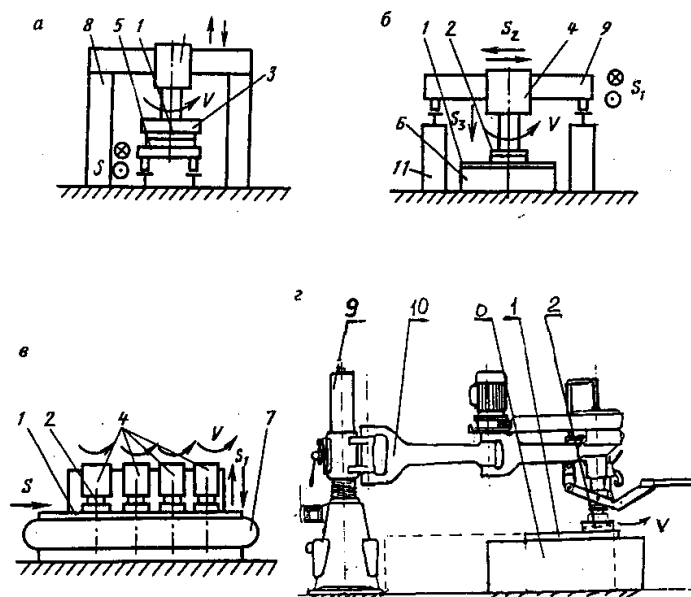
Схемы шлифовально-полировальных станков: а — порталного; б — мостового; в — конвейерного; г — коленно-рычажного (колонкового); 1 — обрабатываемое изделие; 2 — шлифовальный инструмент; 3 — шпиндель; 4 — шлифовальная головка; 5 — тележка; 6 — стол; 7 — конвейер; 8 — портал; 9 — мост; 10 — колонна; 11 — рычажный механизм; V — вращательное движение шлифования; S — рабочая подача; S₁, S₂ — установочные движения
